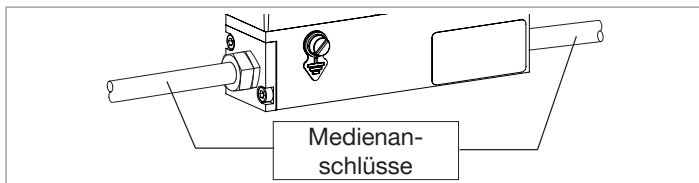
Medienanschlüsse, zum Beispiel Gewindeanschlüsse
